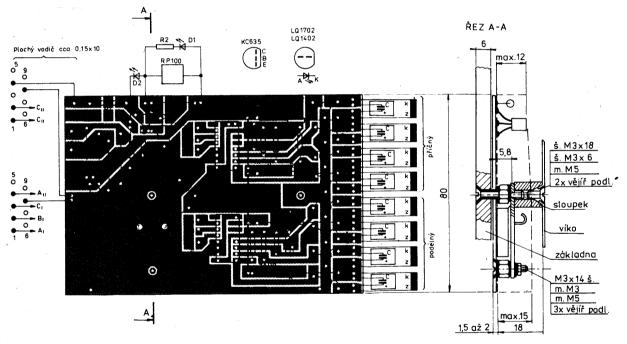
Obrazec plošných spojů desky Y505 (906–2)
